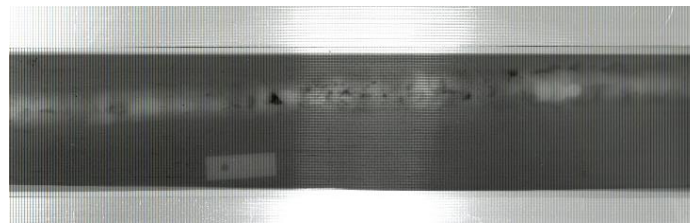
Рентгеновский снимок сварного соединения с дефектами (КСС №1)
